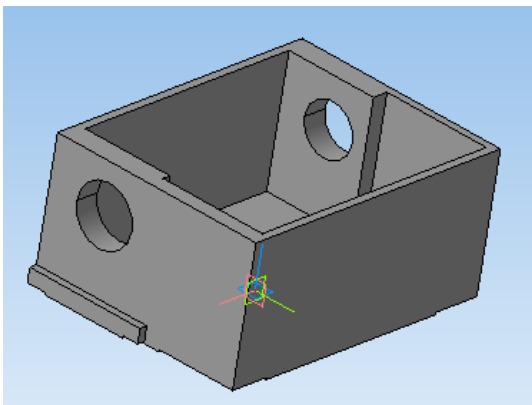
3D модель корпусу шпинделя токарного верстату
